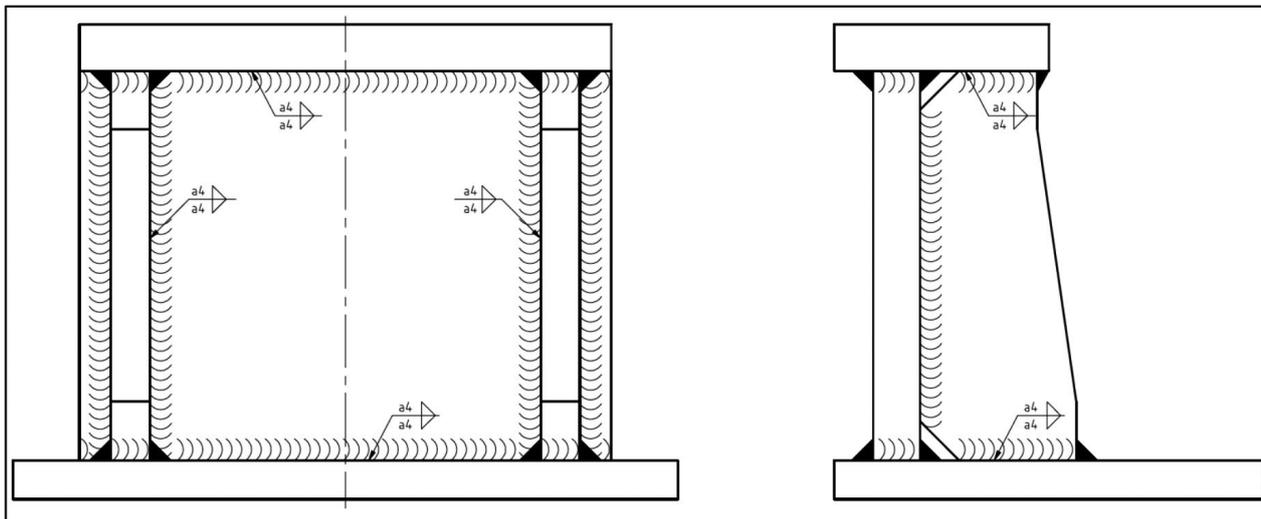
Чертеж сварной конструкции (толщина швов: а4)
